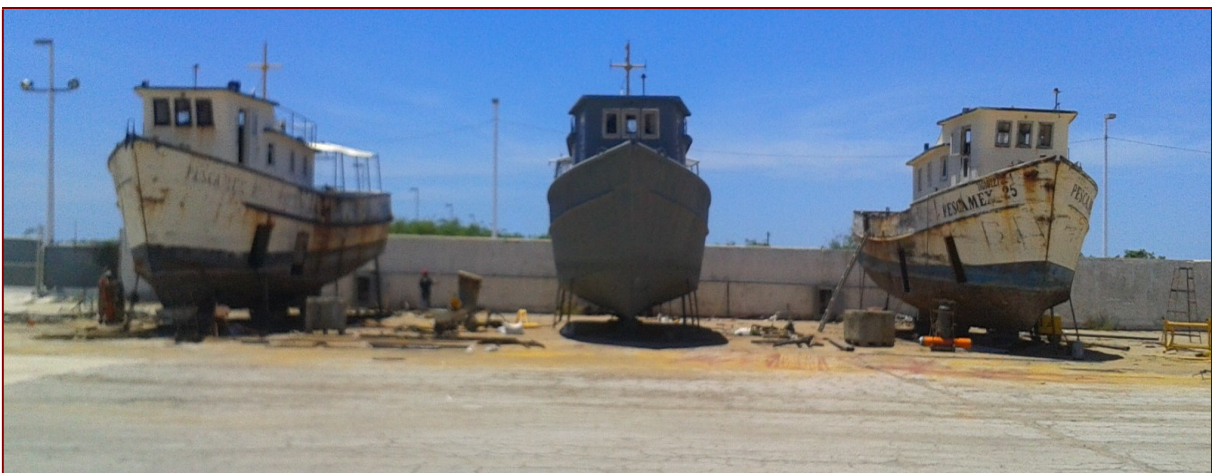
ÁREA DE REPARACIÓN Y CONSTRUCCIÓN.
